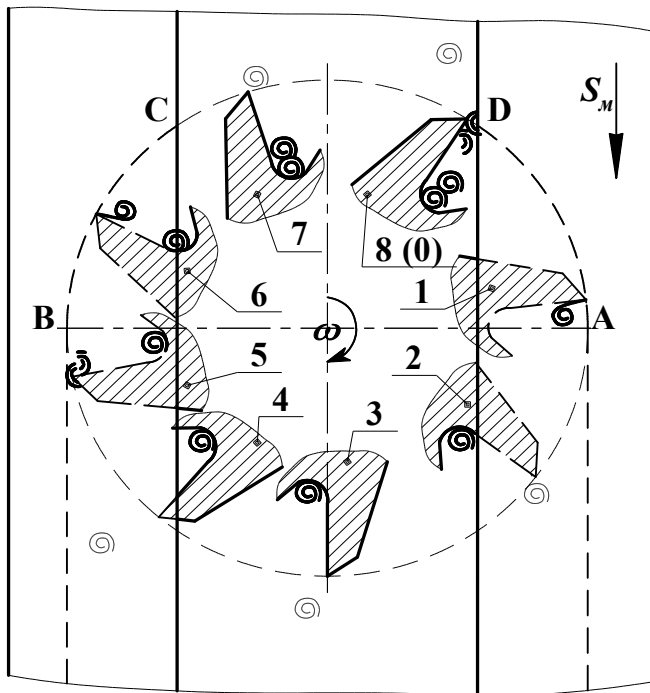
Схема перемещения элемента стружки в пространстве между зубьями фрезы (1...8 - положения зуба в течение одного оборота фрезы)
